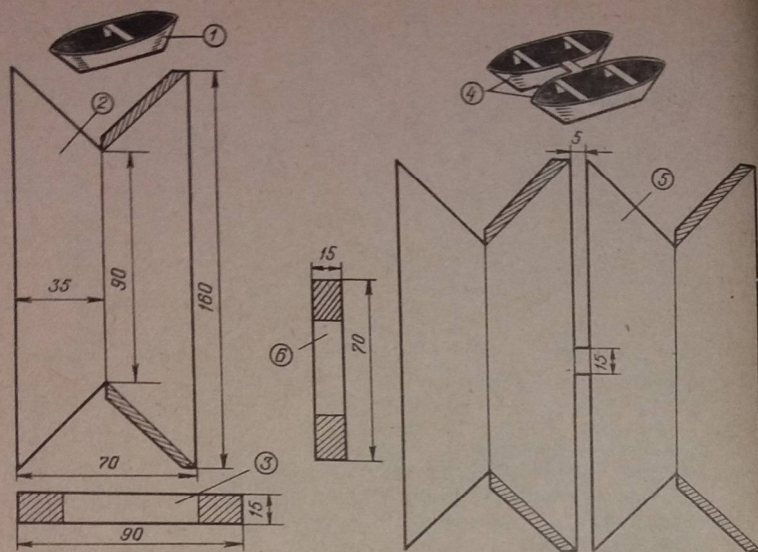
Модели лодочки и катамарана: 1—наглядное изображение лодочки; 2—чертеж развертки корпуса лодочки; 3—чертеж банки (скамейки) для лодочки; 4—наглядное изображение катамарана; 5—чертеж развертки корпуса катамарана; 6—чертеж банки для катамарана
